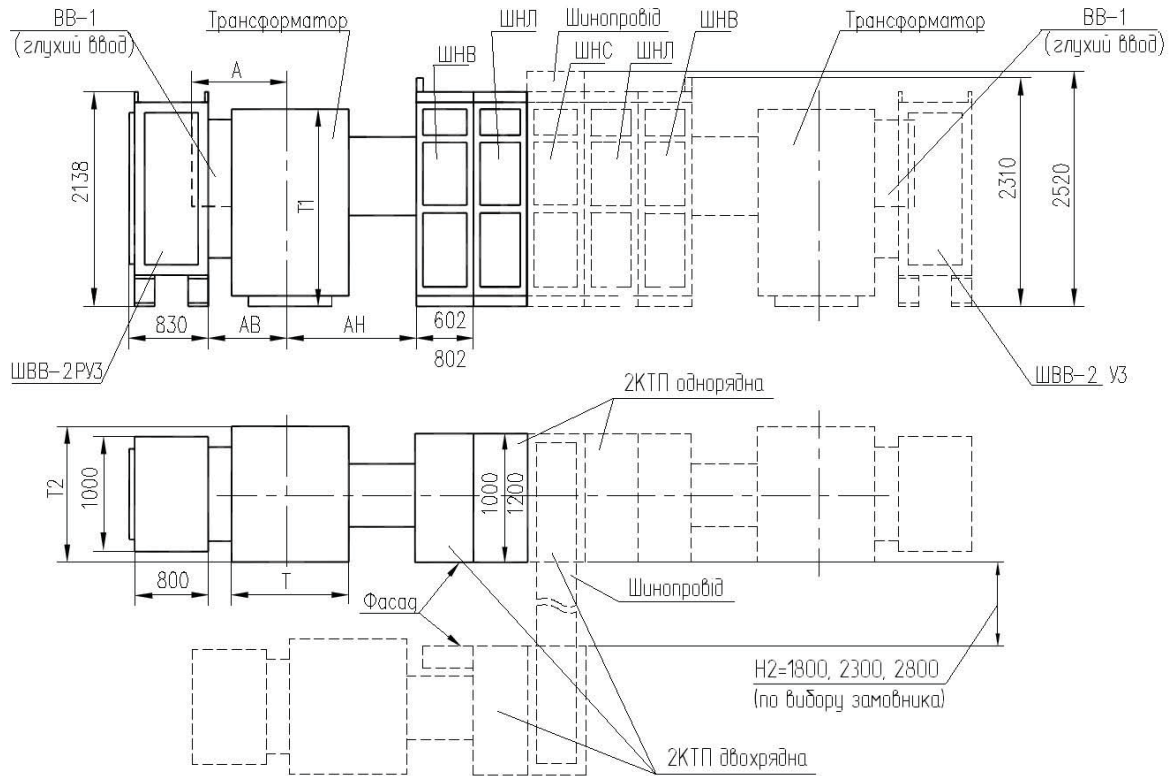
Габаритні розміри КТП-250...2500 з автоматичними вимикачами імпортного виробництва («Schneider Electric», «ABB» і «Siemens») (Габаритні розміри зазначені по основі каркаса.
